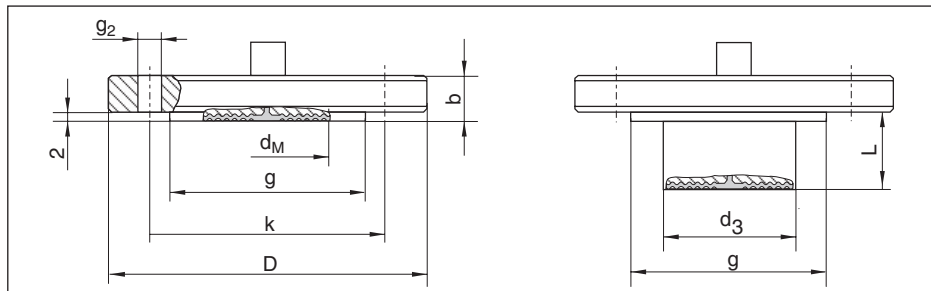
Изолирующая диафрагма с фланцами EN/DIN, присоединительные размеры по EN 1092-1/ DIN 2501
